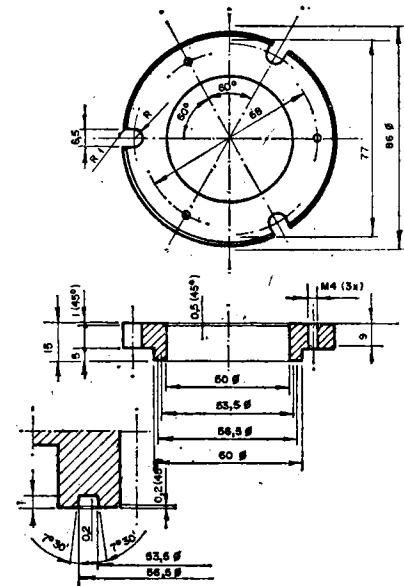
Aro de presión del recipiente, detalles en corte vertical y plano
